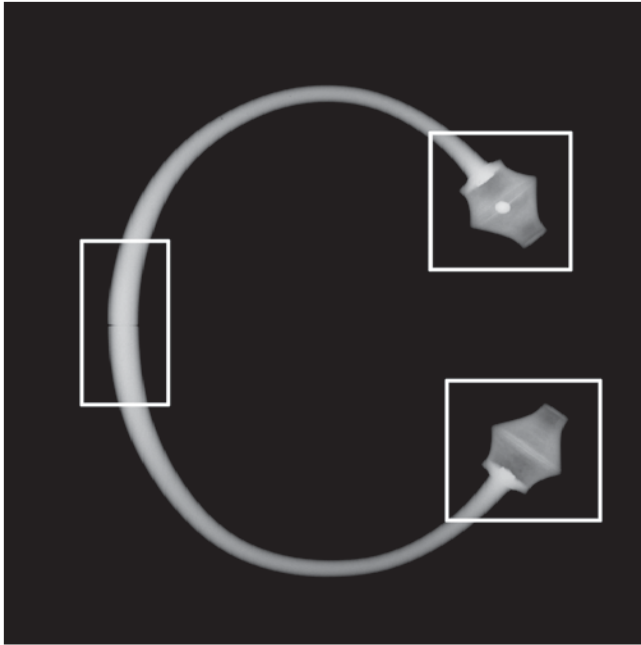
Deficiencia de la soldadura que intenta disimular el corte.
